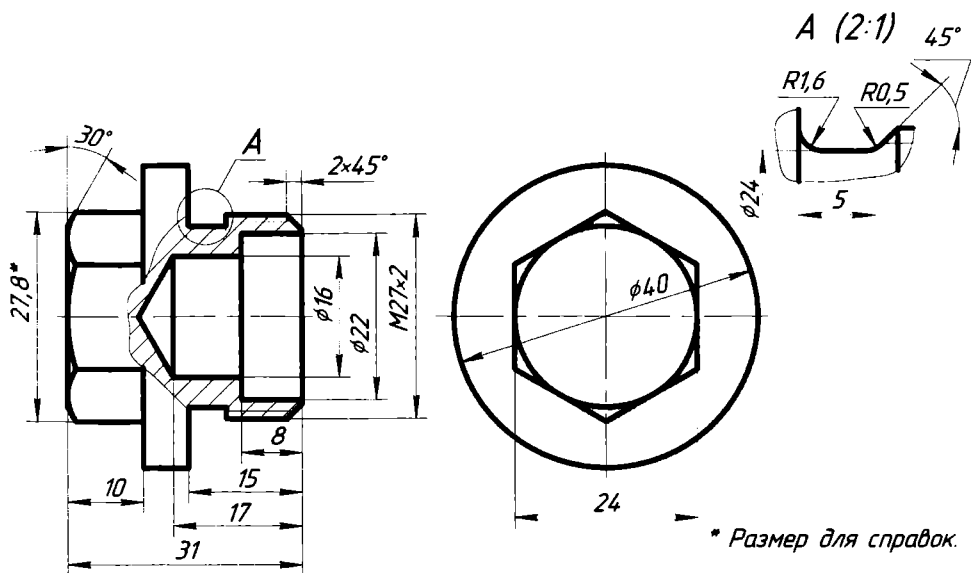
Принятые упрощения на чертежах деталей с элементами типа гайки и внешней резьбы с проточкой
